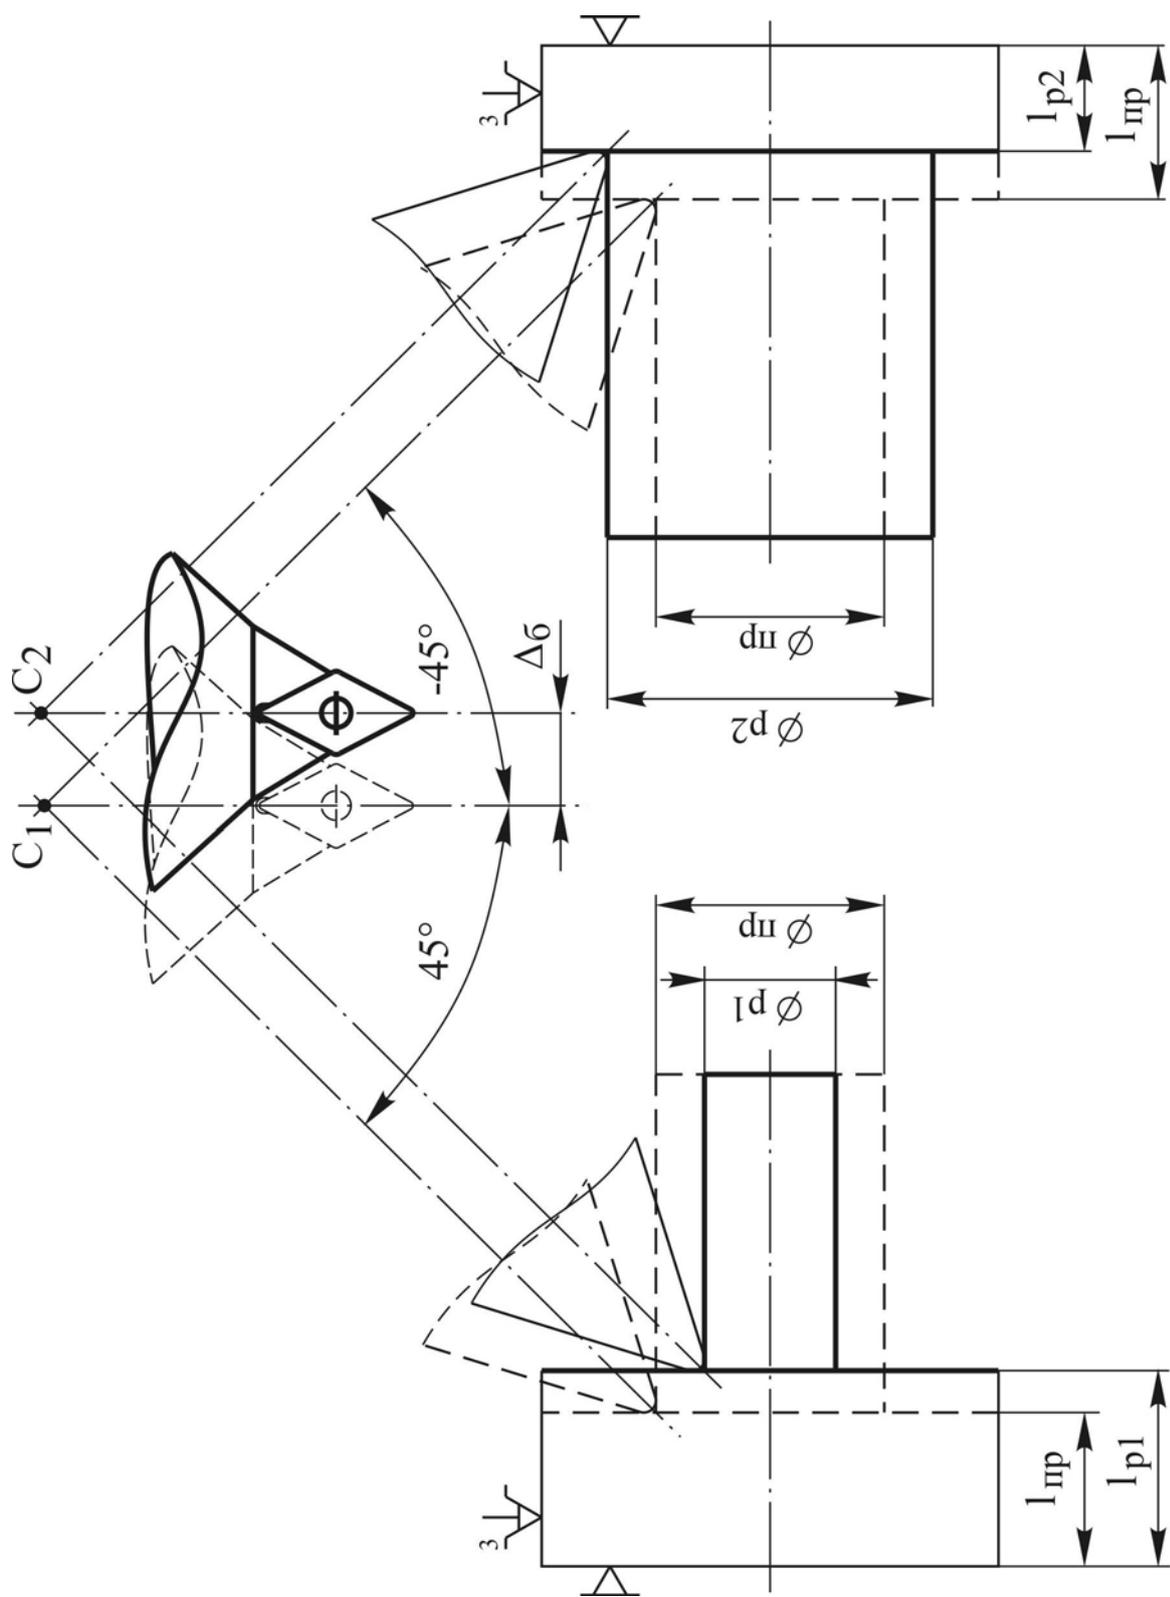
Схема возникновения погрешности обработки от погрешности базирования резцовой головки во фрезерном шпинделе
